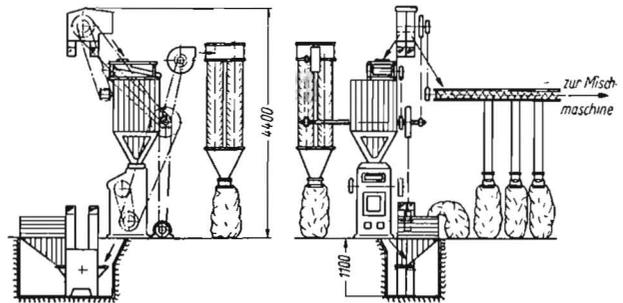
Schrotmaschinenanlage [VEB (K) „Fanal“]
